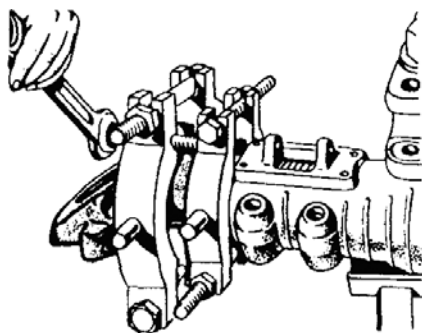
Выпрессовка корпуса верхней конической пары из крышки дифференциала.
